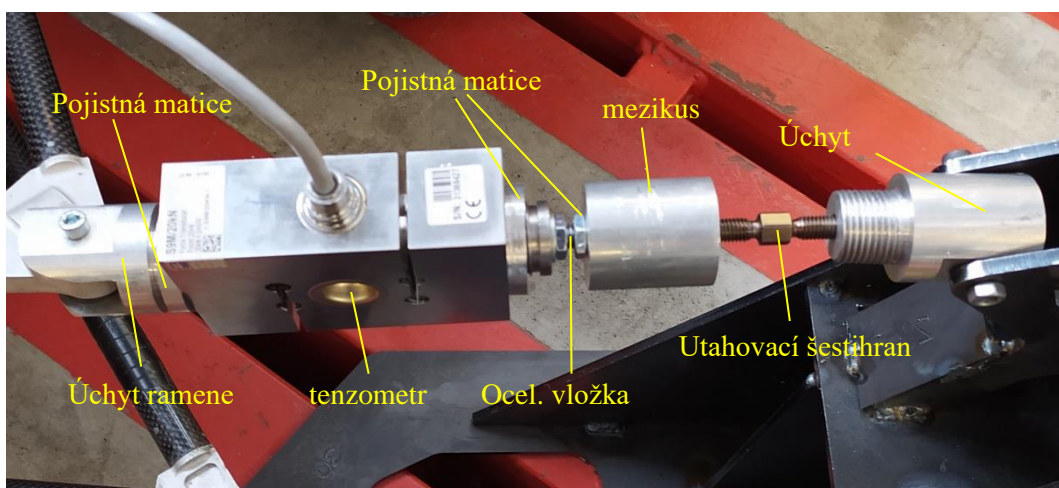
Finální upevnění monokoku k drážkované podlaze
